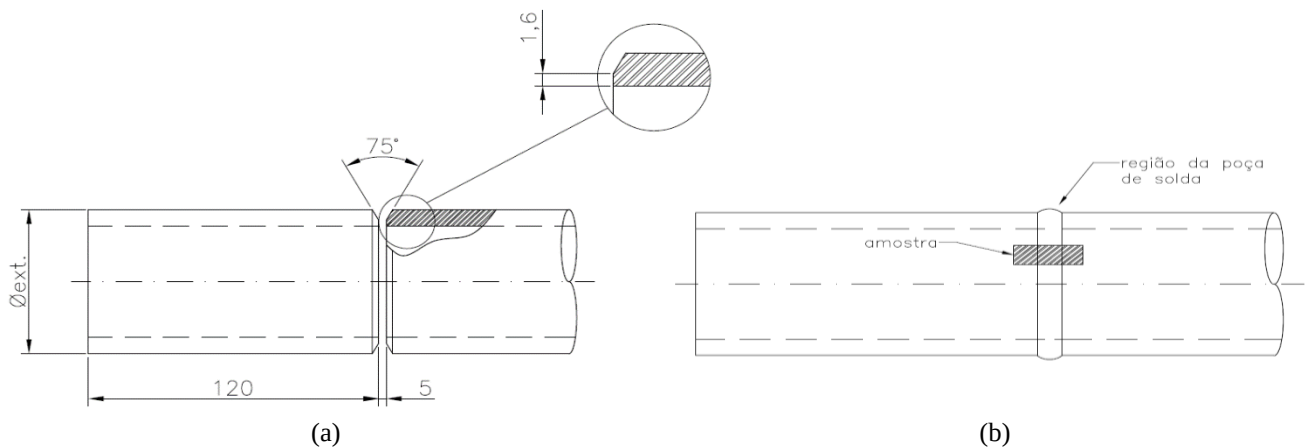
Configuração para união dos tubos por solda (a); região de corte das amostras (b)
